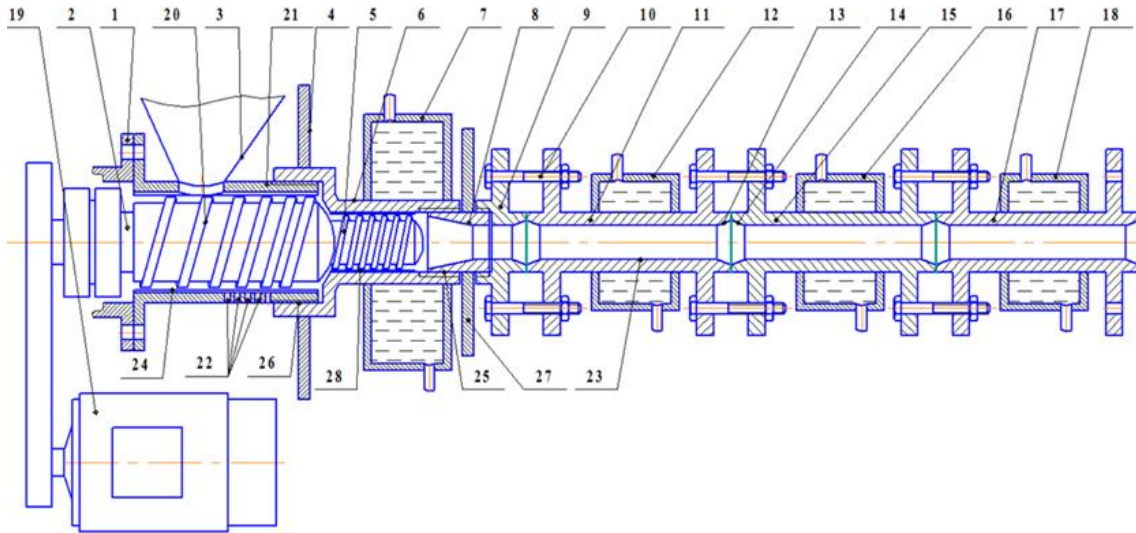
Схема шнекового прес-екструдера для отримання паливних брикетів з пристроєм остаточного формування: 1 – підшипниковий вузол; 2 – вал приводу; 3 – бункер; 4 – фіксатор; 5, 20 – шнек; 6 – камера дожиму; 7, 12, 16, 18 – сорочка охолодження; 8 – матриця; 9 – пристрій остаточного формування; 10 – болт; 11, 15, 17 – секції труб; 13, 14 – масло згінні фаски; 19 – електродвигун; 21 – пресуюча камера; 22 – отвори для відводу масла; 23 – труба; 24, 28 внутрішні ребра; 25, 26 – різьбове з'єднання; 27 – рукоятка
